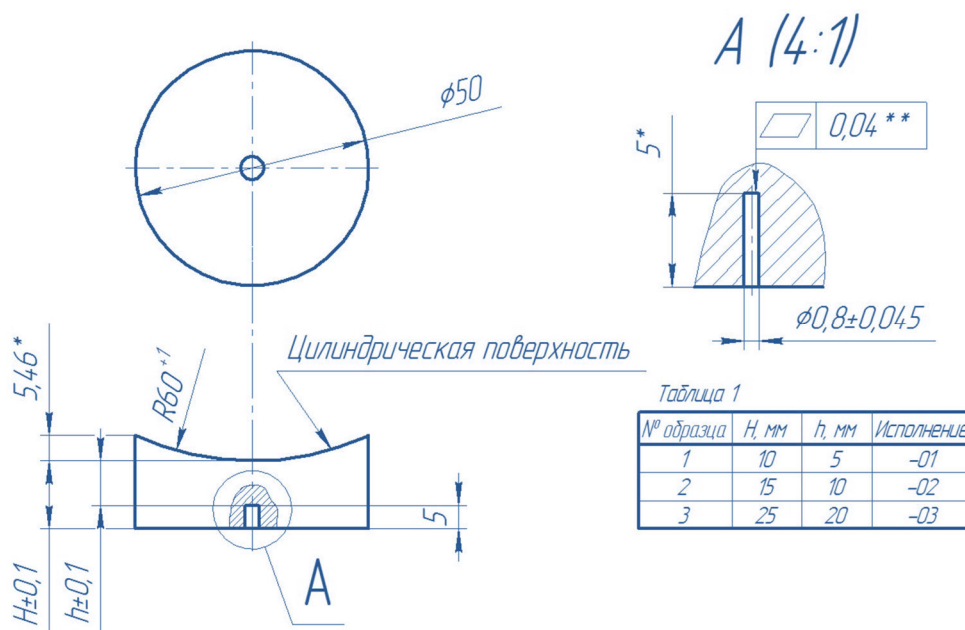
Модельные образцы из титанового сплава с контрольными отражателями и криволинейной поверхностью ввода
